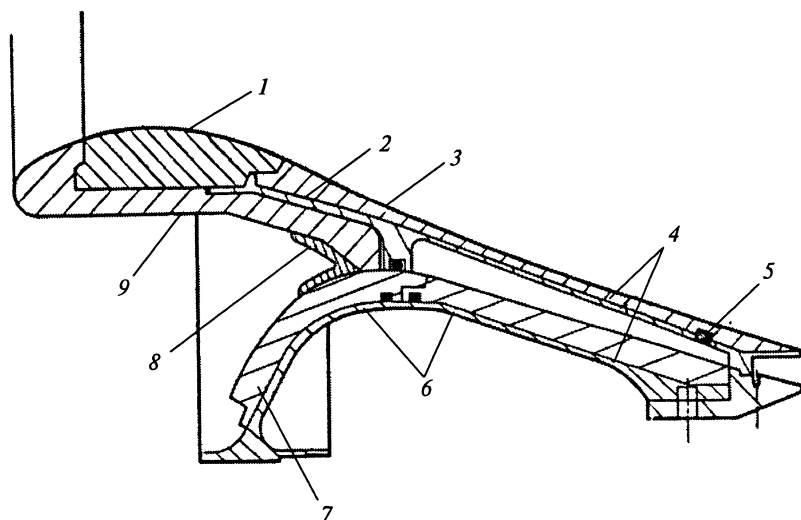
Конструктивная схема сбрасываемого стартового сопла:
